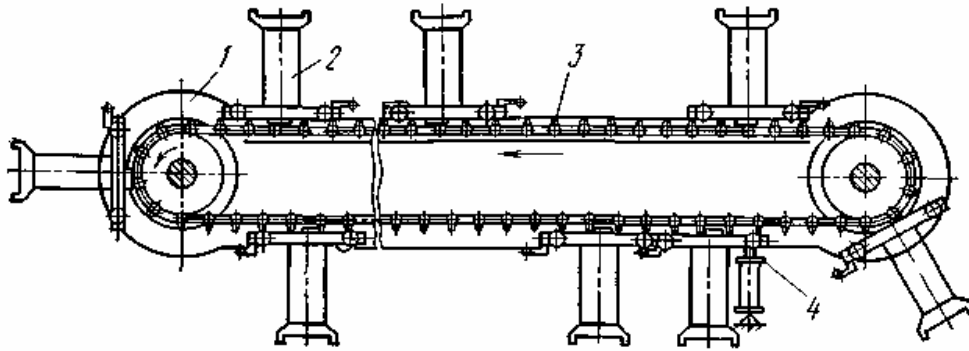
Тележечный конвейер для разборки (сборки) агрегатов: 1 – направляющие; 2 – грузонесущая тележка; 3 – тяговая цепь; 4 – останов
